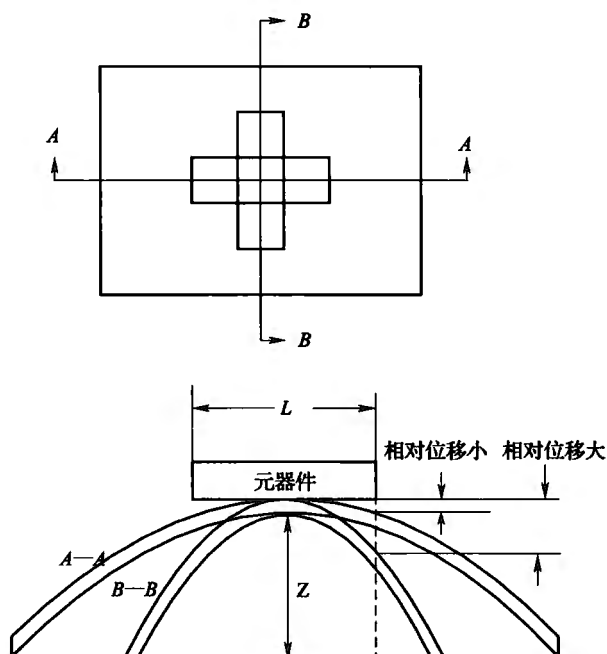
器件平行于 PCB 长边安装时器件与 PCB 间的相对运动会减少
